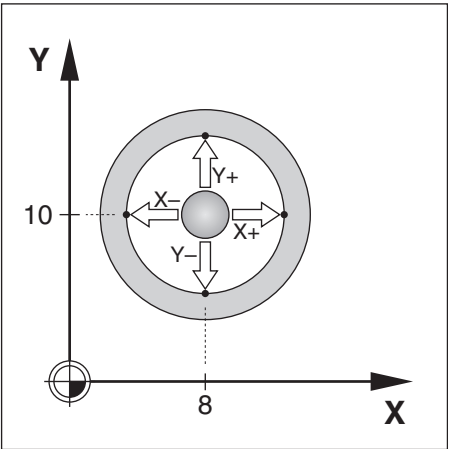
Apalpação da parede interior do círculo para cálculo da posição do ponto central do círculo
